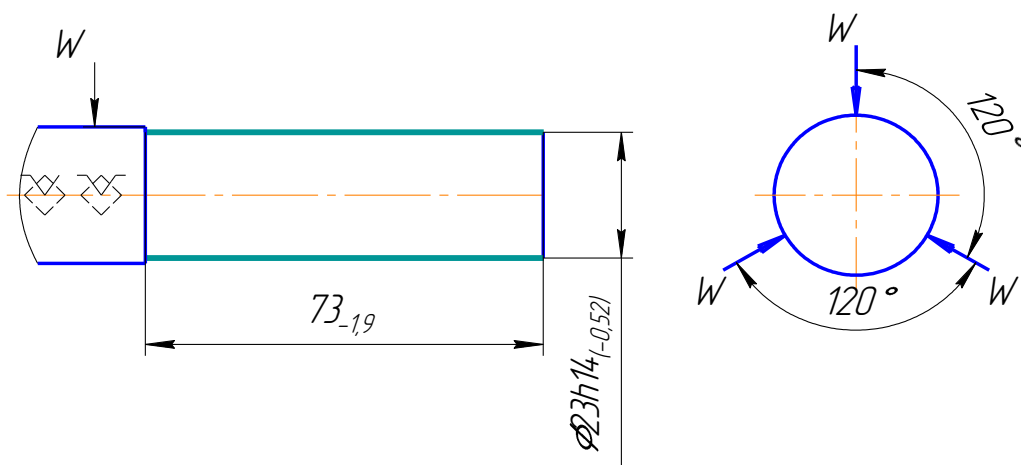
Принципиальная схема зажима заготовки в приспособлении с
